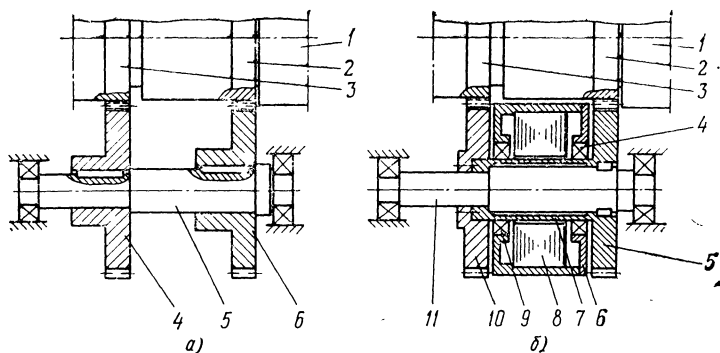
Часть кинематической цепи шпинделя токарного станка 1А616ФЗ:
